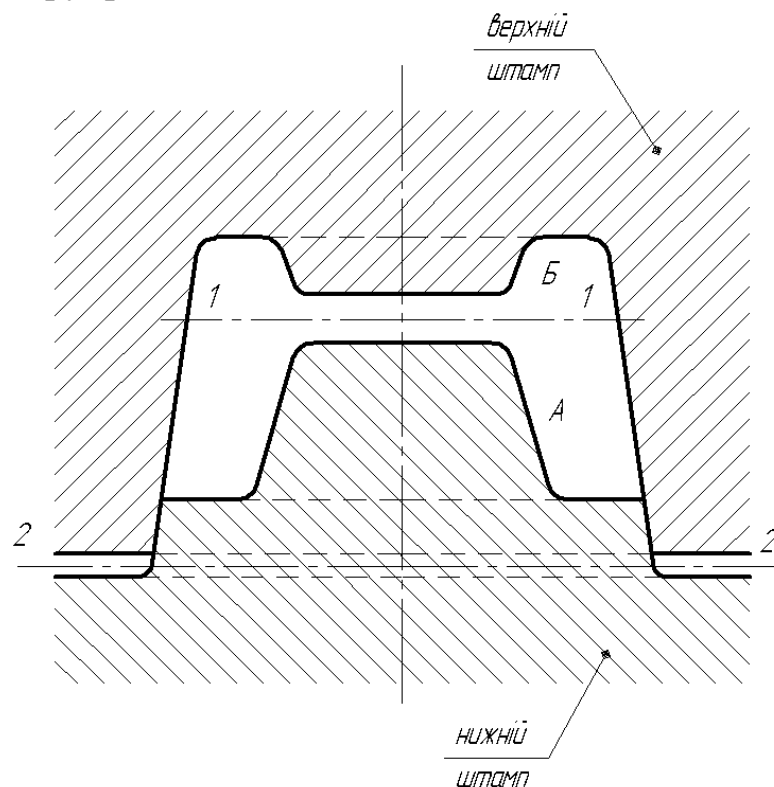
Схема штамованої заготовки в закритому штампі:
